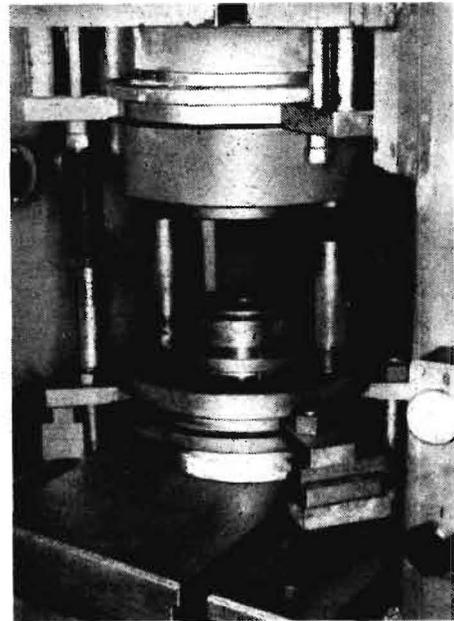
Warmformpressen zur Aufarbeitung von Kugelzapfen (links: Unterwerkzeug, rechts: Oberwerkzeug)
